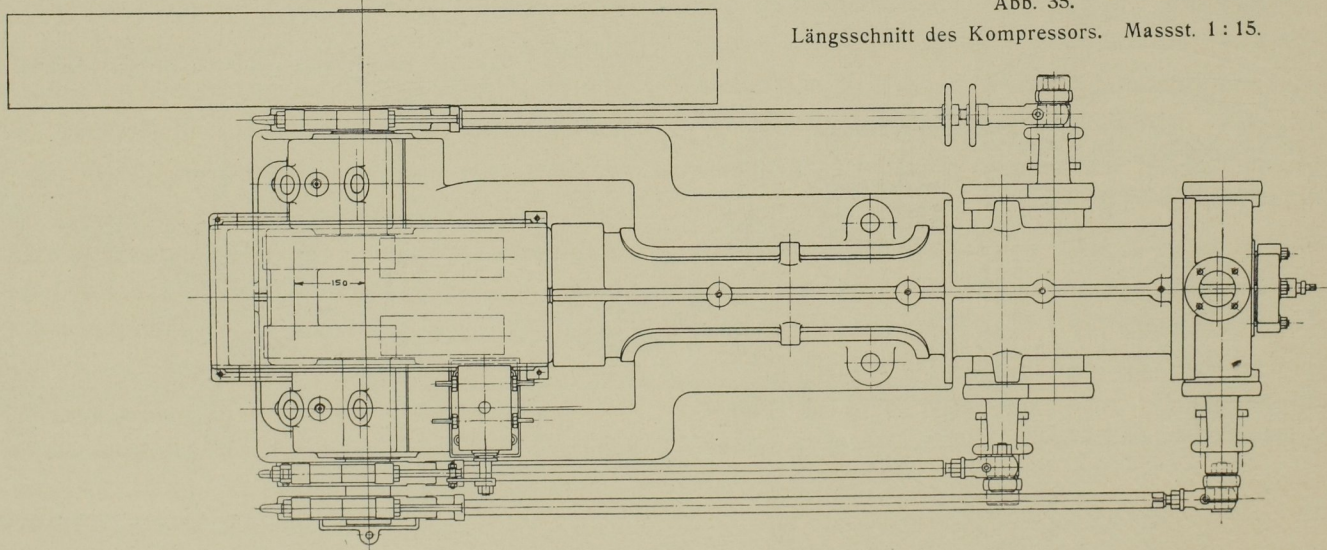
Grundriss des Kompressors. Masst. 1 : 15.
